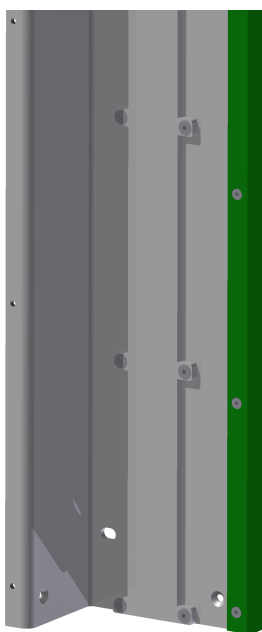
Vedení vodících kol hřídele podavače po bočním vedení
